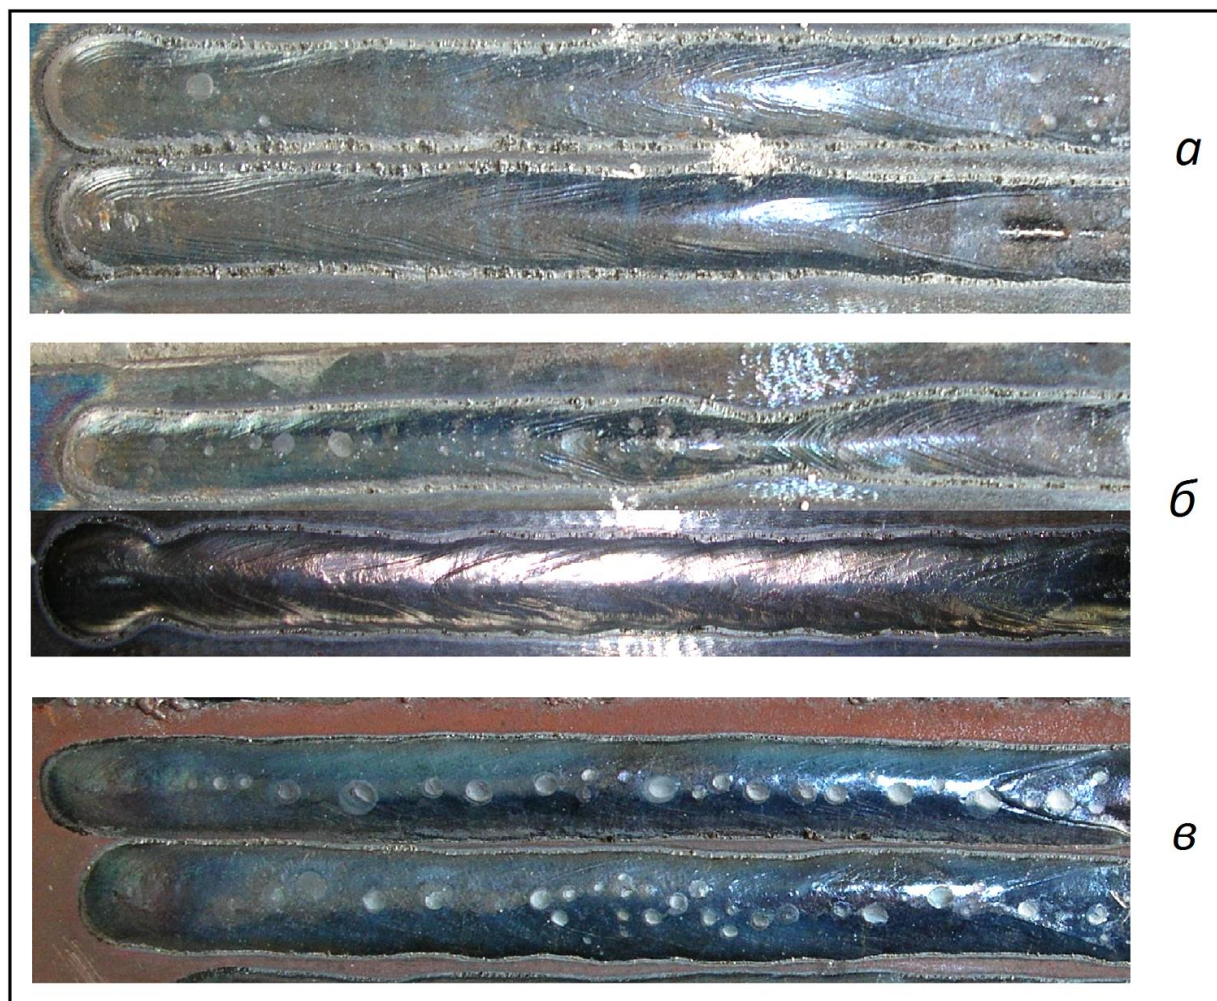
Браковочные дефекты сварных швов при испытании флюсов: *а* – пригар шлака по краям валика; *б* – нарушение формы сварного шва; *в* – пятна «побитости»
